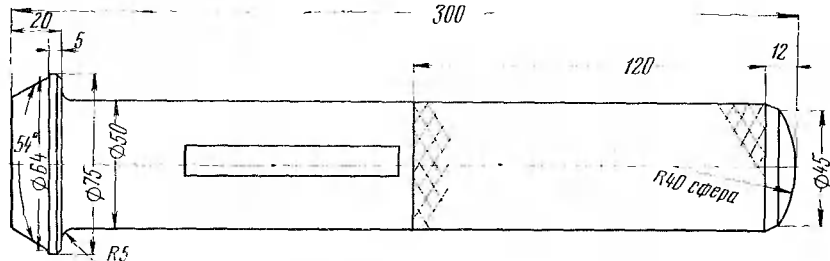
Оправка для запрессовывания наружного кольца подшипника винта в картер рулевого механизма
